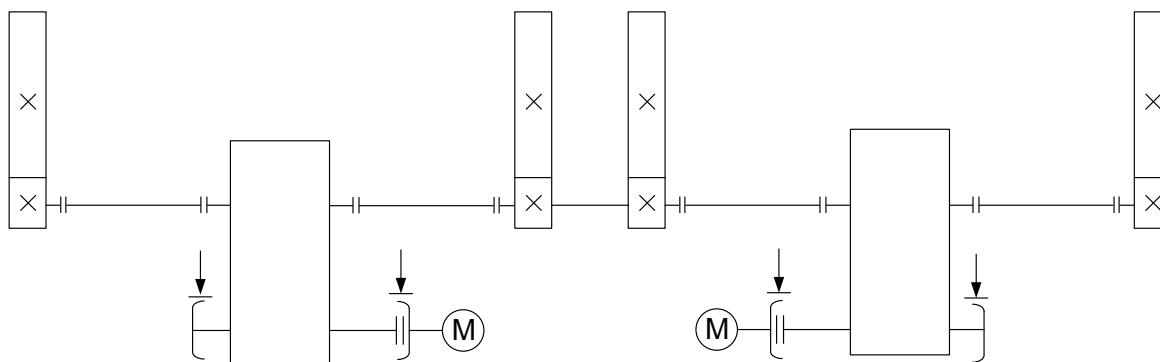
Кинематическая схема вагоноопрокидывателя
